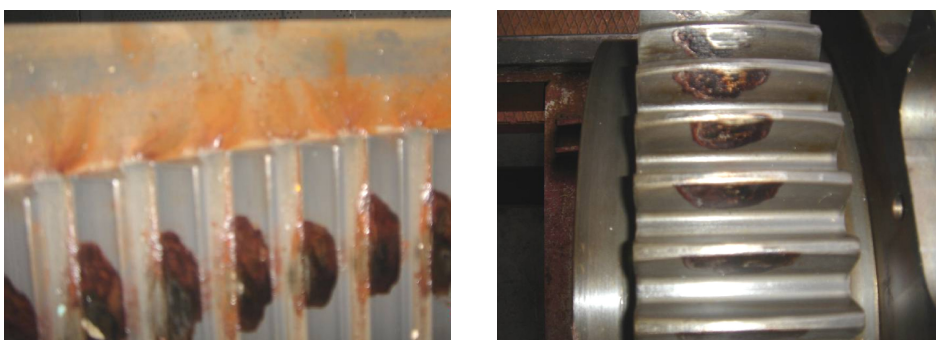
Аварийный останов и простой ЭГПА2-12,5/76-1,5 с центробежным нагнетателем ЦБН 285-22-1 из-за дефектов зубчатой муфты (схватывания зубьев): а – полушестерня зубчатая (сторона ГЭД); б – зубчатая втулка ГЭД
